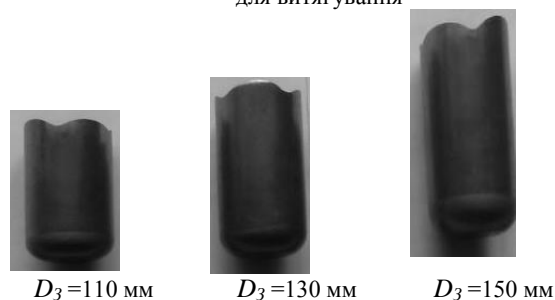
Деталі, які отримані із заготовок різного діаметра D_3
